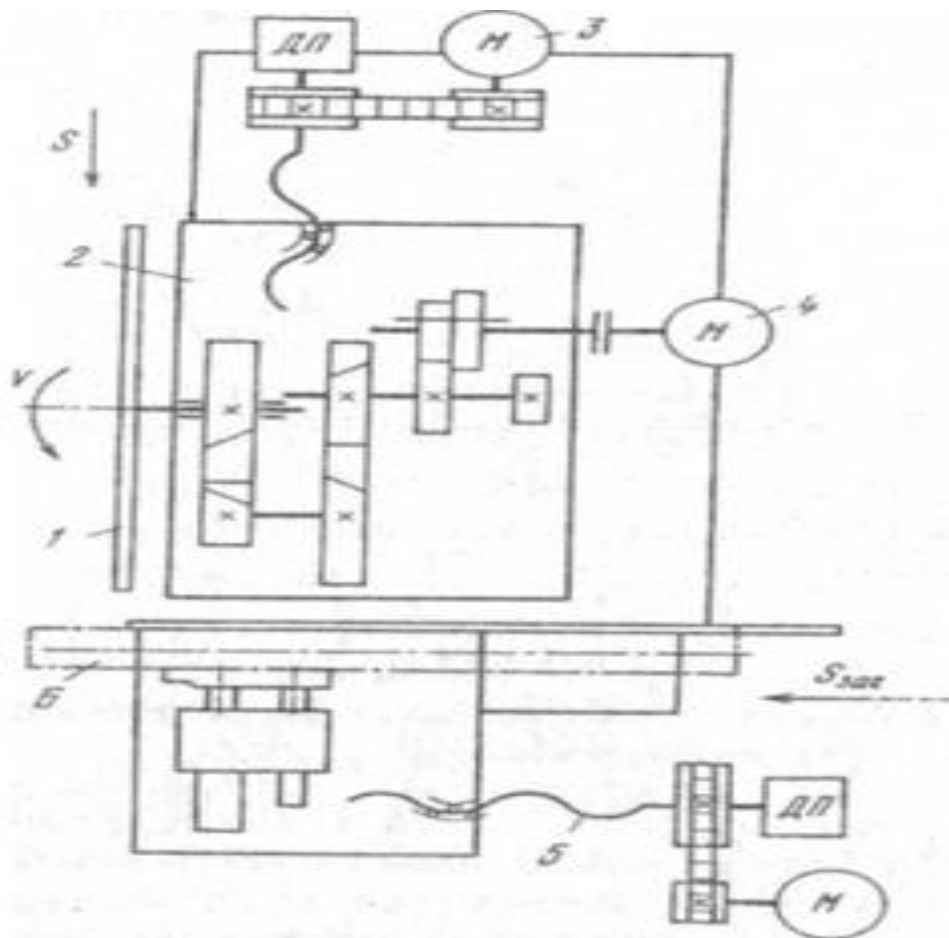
Кинематическая схема отрезного станка, работающего дисковой пилой: 1 – пила, 2 – коробка скоростей, 3 – привод радиальной подачи фрезы, 4 – электродвигатель главного движения, 5 – привод подачи заготовки, 6 - заготовка, V – скорость резания, S – рабочая подача, $S_{заг}$ – подача заготовки, ДП – датчик положения.
